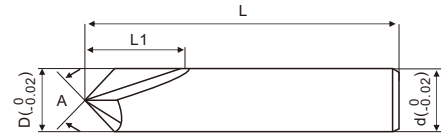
铝用不涂层 AL Uncoated	Fig.2	黑色涂层 Black Coating	Fig.3	古铜色涂层 Bronze Colored Coating	钻尖角度 A Drill point angle	刃径 D Outside Diameter	柄径 d Shank Diameter	刃长 L1 Flute Length	总长 L Total Length	Order Number
